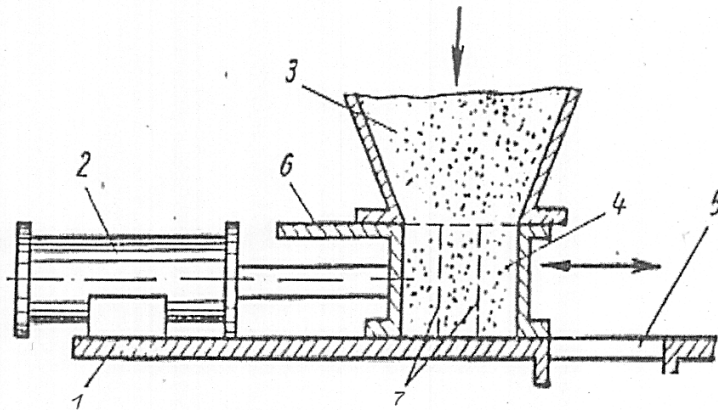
Схема дозатора камерного типу: 1 – напрямна плита; 2 – пневмоциліндр; 3 – бункер; 4 – об'ємна камера; 5 – розвантажувальна лійка; 6 – затвор; 7 – пази
